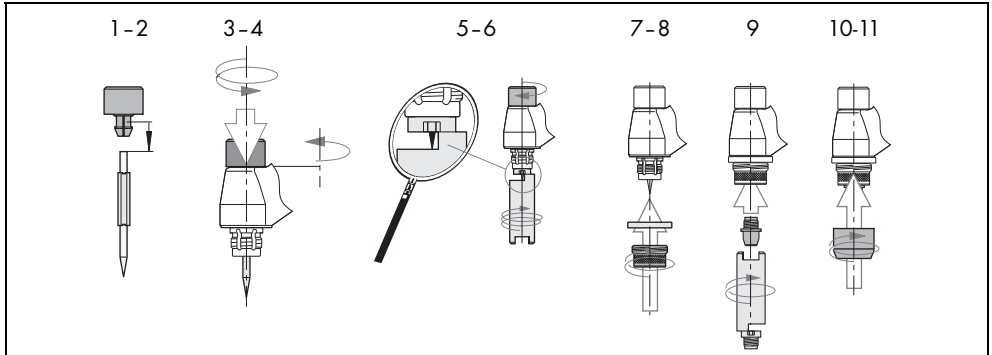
Opérations pour l'équipement du corps de torche ABIPLAS® WELD 150 CT20
